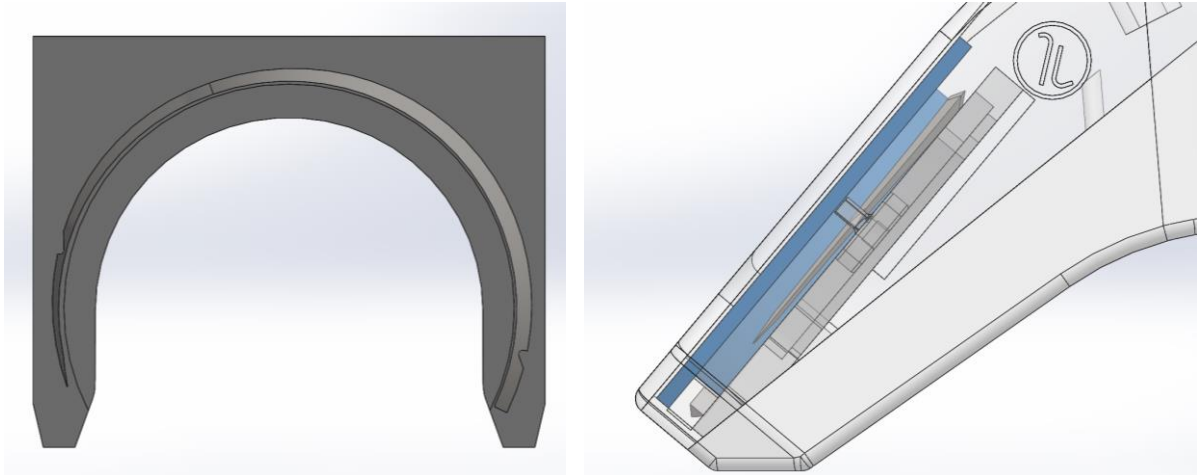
Vista en planta de la guía de la aguja (izq) y su posición en el dispositivo (dcha)
